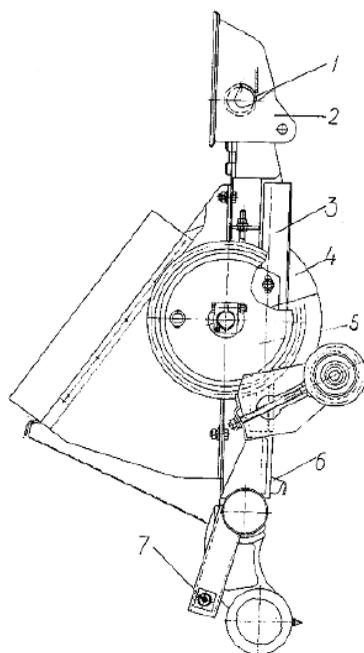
Проставка: 1 – верхняя несущая труба;
